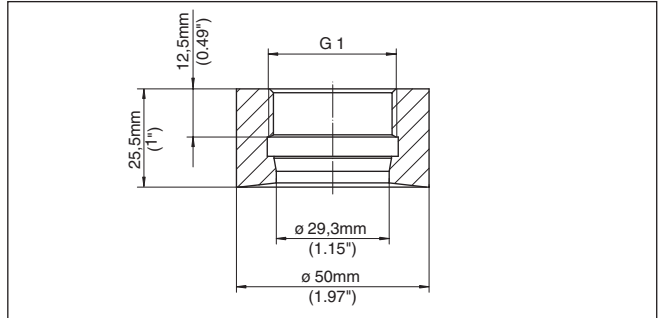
Maße Einschweißstutzen G1, Hygiene - VEGABAR 17
